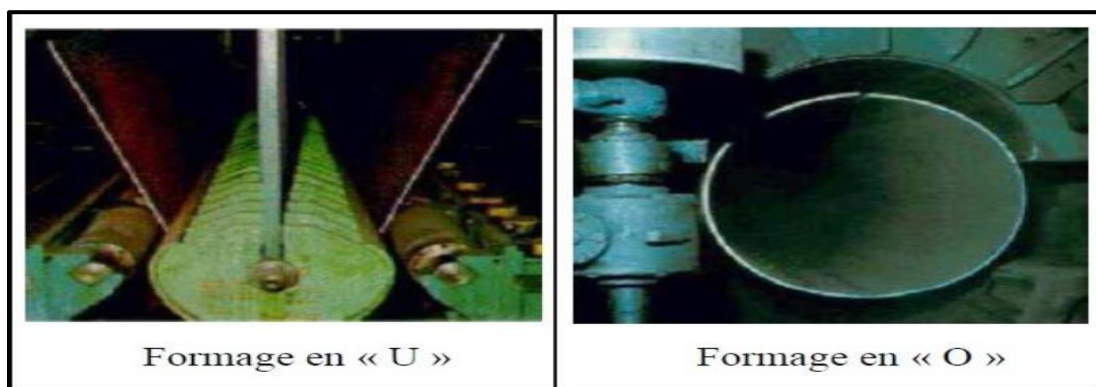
La mise en forme des tubes par le procédé « UOE » [6]
